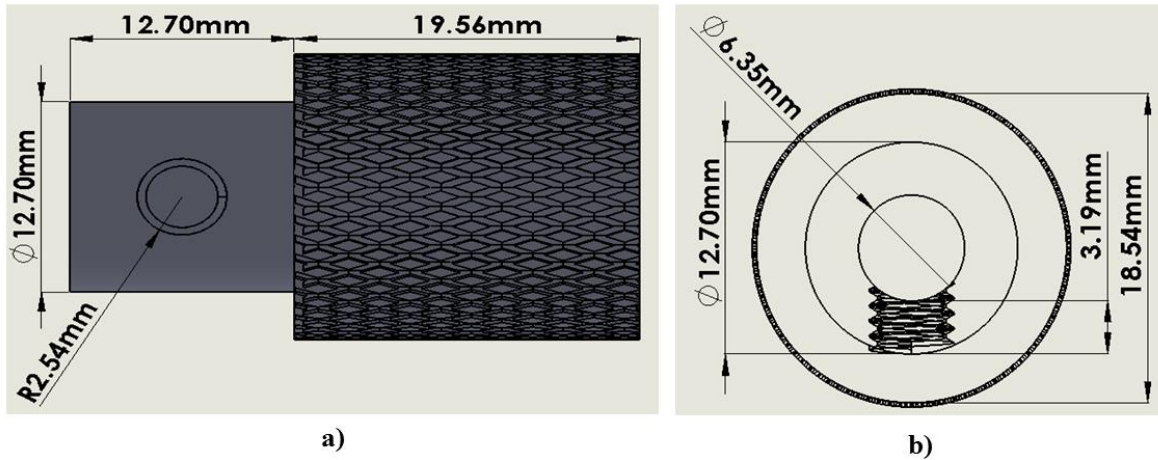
a) Vista lateral de las cabezas de los tornillos, b) Medidas frontal de la cabeza del tornillo.
